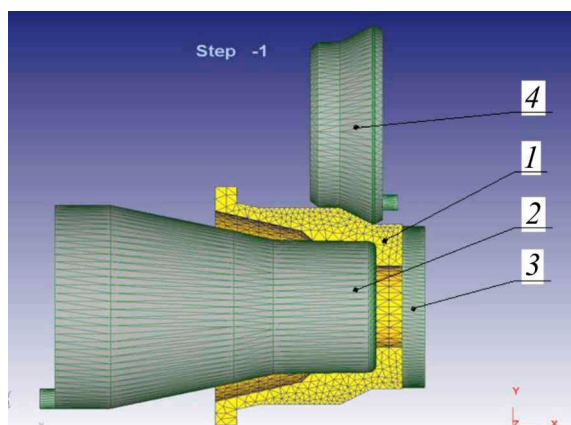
Схема раскатки: 1 – заготовка, 2 – оправка, 3 – прижим, 4 – ролик
